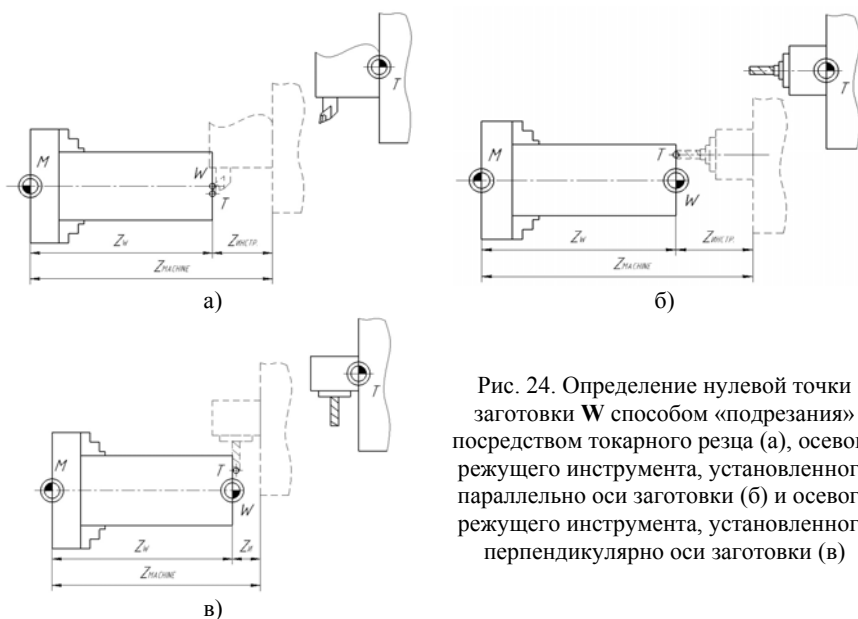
Определение нулевой точки заготовки W способом «подрезания» посредством токарного резца (а), осевого режущего инструмента, установленного параллельно оси заготовки (б) и осевого режущего инструмента, установленного перпендикулярно оси заготовки (в)
